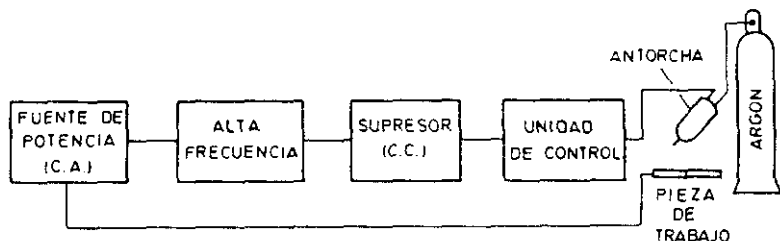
Esquema del Equipo de Soldadura TIG.
